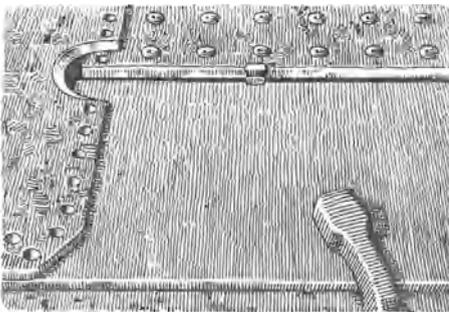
Zur Schweißung vorbereiteter Flicker einer Feuerbüchse.
